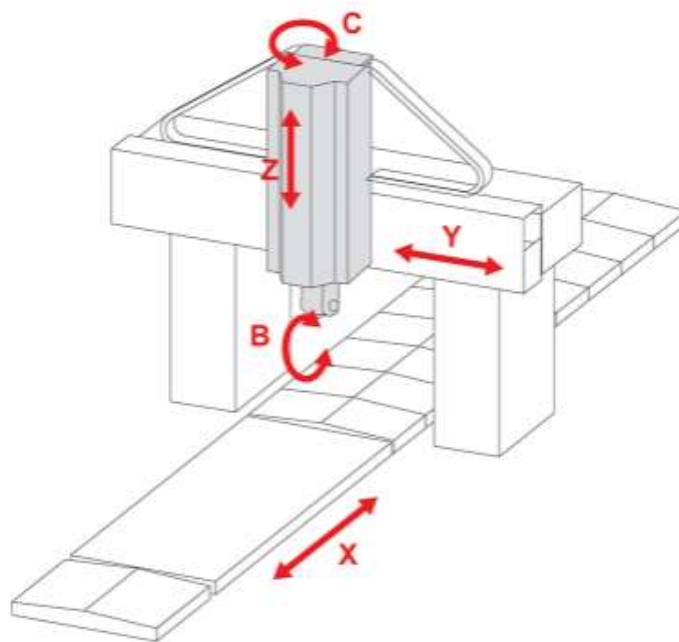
Портальний фрезерний верстат з ЧПК з рухомим столом
